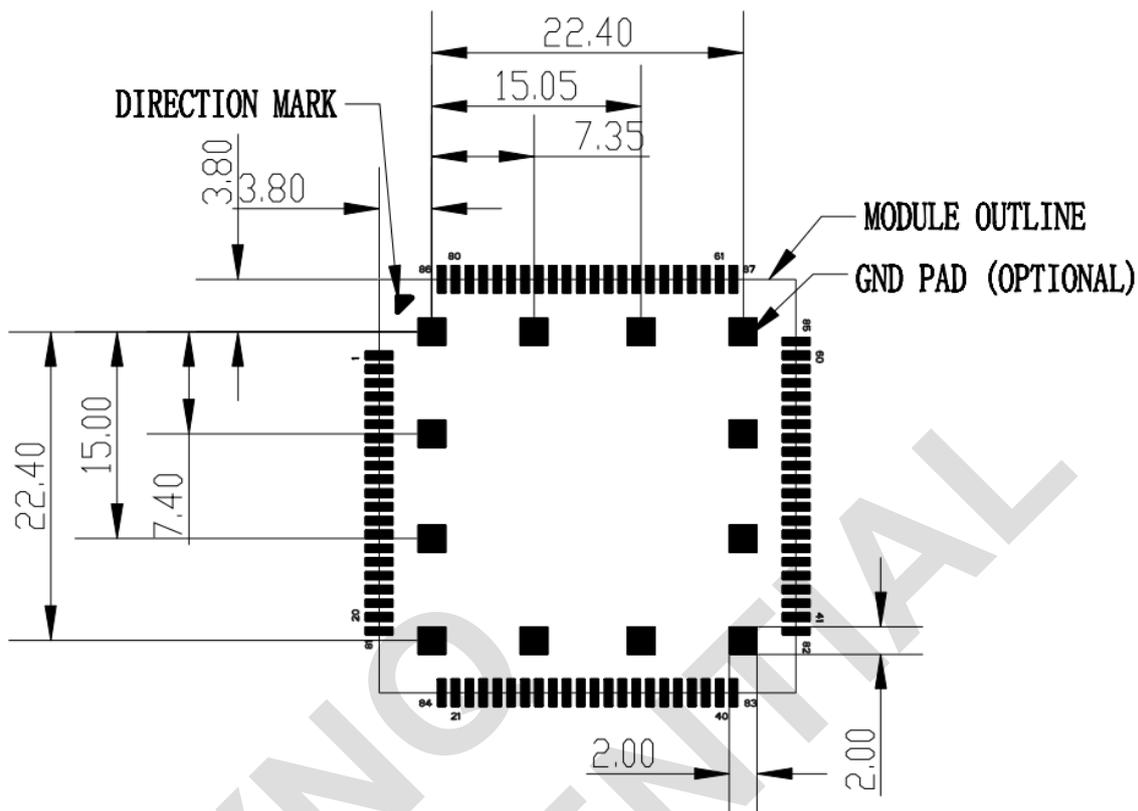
推荐焊盘钢网Top view (detail B)
